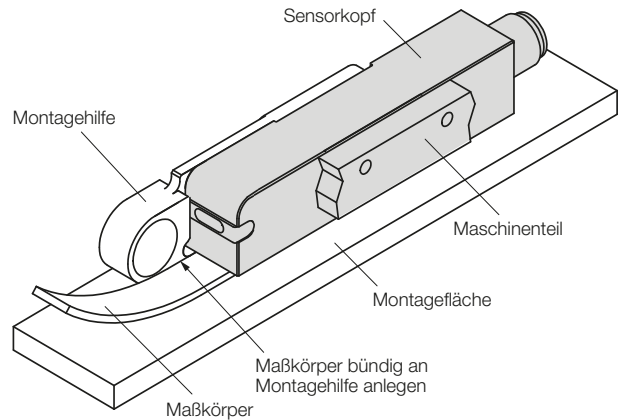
Montagehilfe BAM TO-ML-006-S1G (Bestellcode BAM0256) befestigen (Links- oder rechtsseitige Befestigung ist möglich, Abbildung zeigt rechtsseitige Befestigung)
